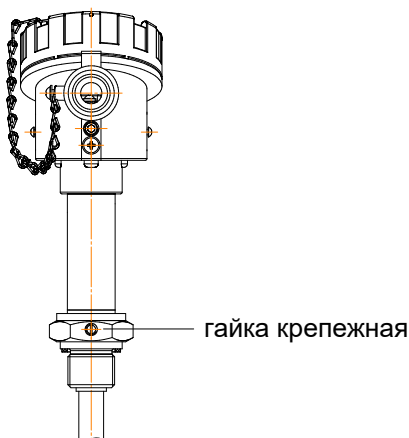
Расположение крепежной гайки на корпусе УПМ-51
